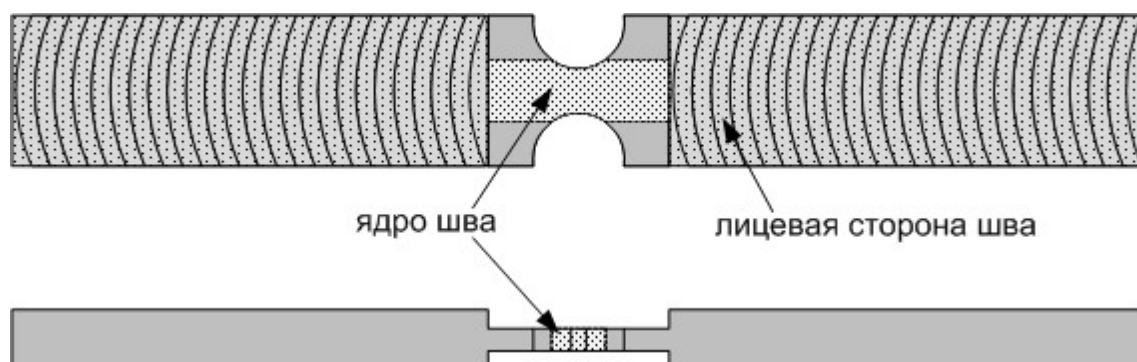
Схема вырезки образцов для испытаний из ядра сварного соединения
